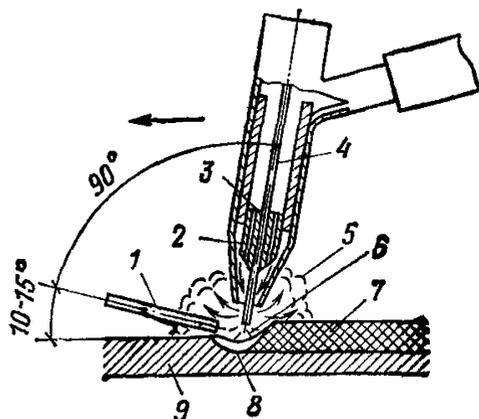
Схема сварочной горелки и зоны сварки неплавящимся электродом
